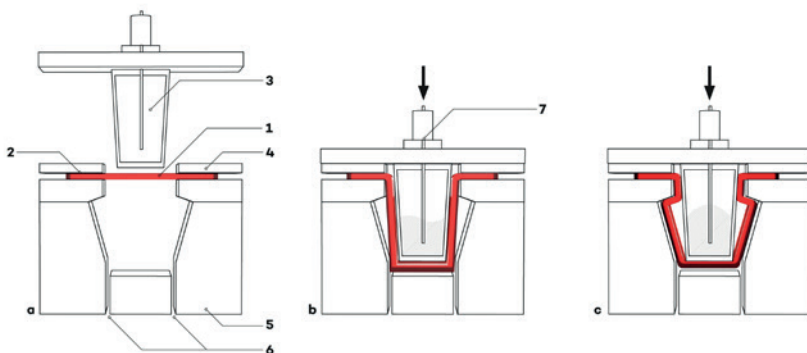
Blasformen in ein Negativ-Formwerkzeug mit mechanischer Vorstreckung: PLEXIGLAS® (1), Dichtungsrand (2), Stempel (3), Spannrahmen (4), Negativ-Formwerkzeug (5), Entlüftungskanäle (6), Druckluftanschluss (7)
